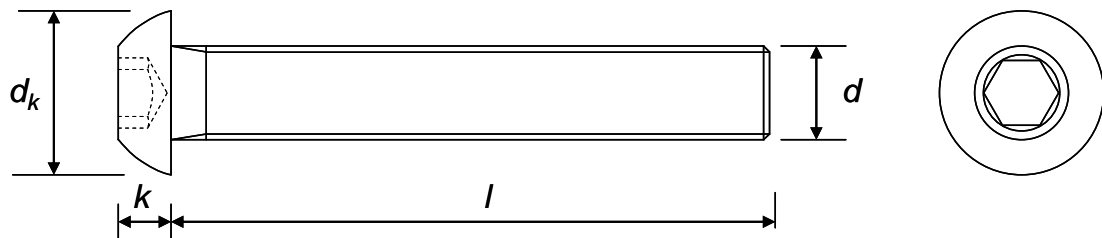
Halbrundkopfschraube mit Innensechskant
